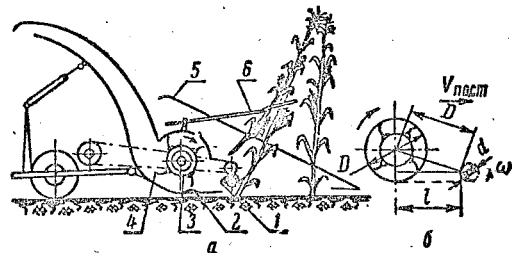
Схема роторной косилки с приспособлением для скашивания высоких стеблей кукурузы.
